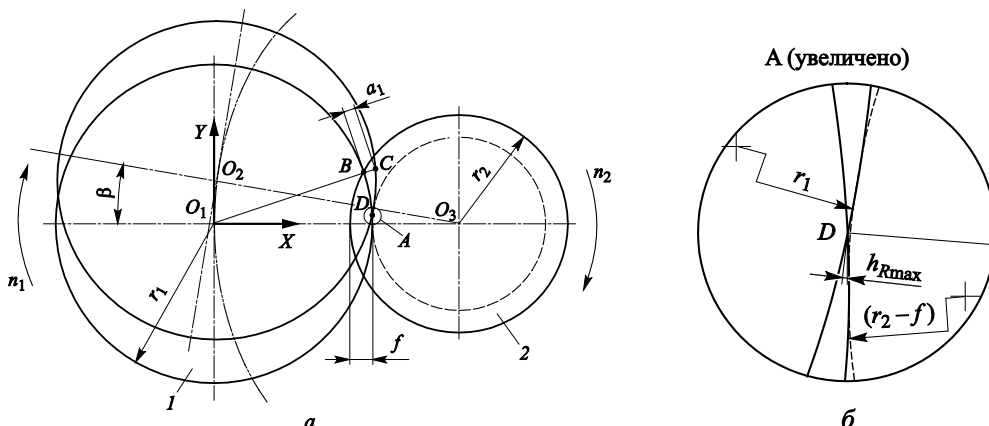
Схема расчета шероховатости поверхности в продольном направлении: 1 — ШК; 2 — заготовка
